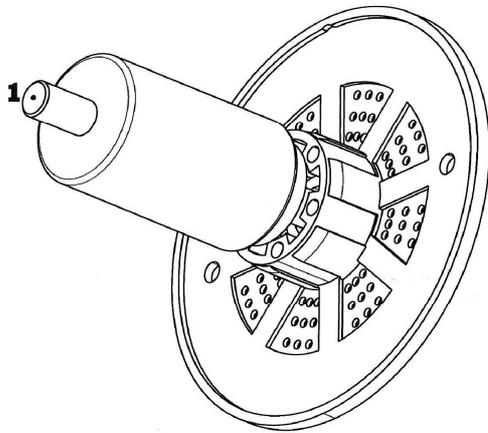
Rotor vom Eco Runner mit Abdeckplatte
